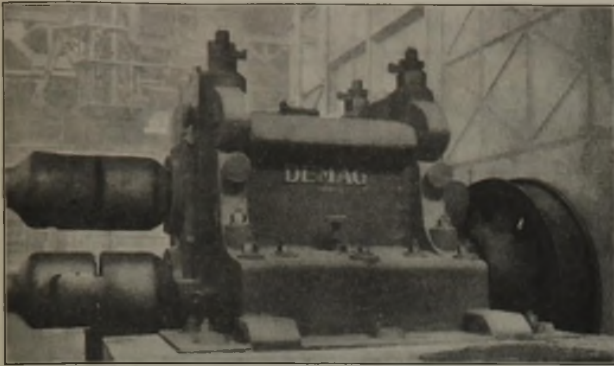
Kammwalzgerüst mit Bibbykupplung für 950er Blockstraße.
